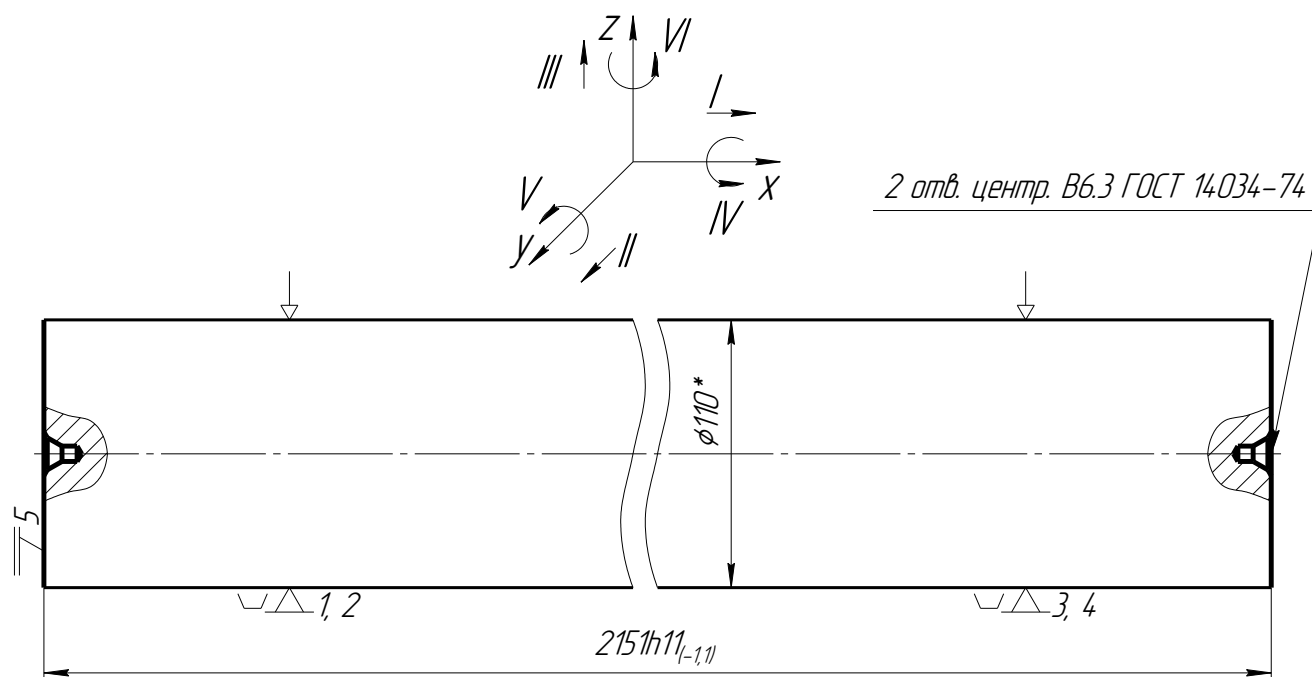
Схема установки заготовки на призмы с прижимом прихватами
